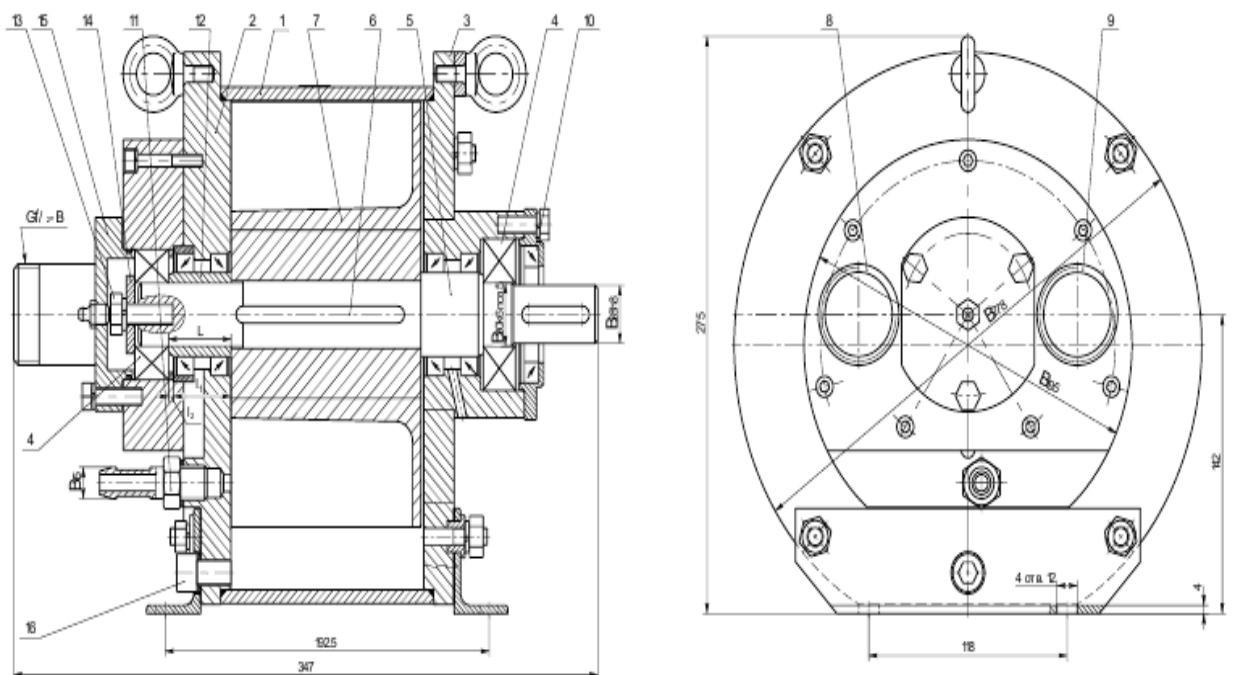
Водокільцевий вакуумний насос ВВН-70: 1 – корпус; 2 – лобовина ліва; 3 – лобовина права; 4 – підшипник; 5 – вал; 6 – шпонка; 7 – колесо; 8 – патрубок всмоктувальний; 9 – патрубок вихлопний; 10 – манжета; 11 – патрубок подавання води; 12 – втулка; 13 – болт; 14 – шайба; 15 – кришка; 16 – пробка.
